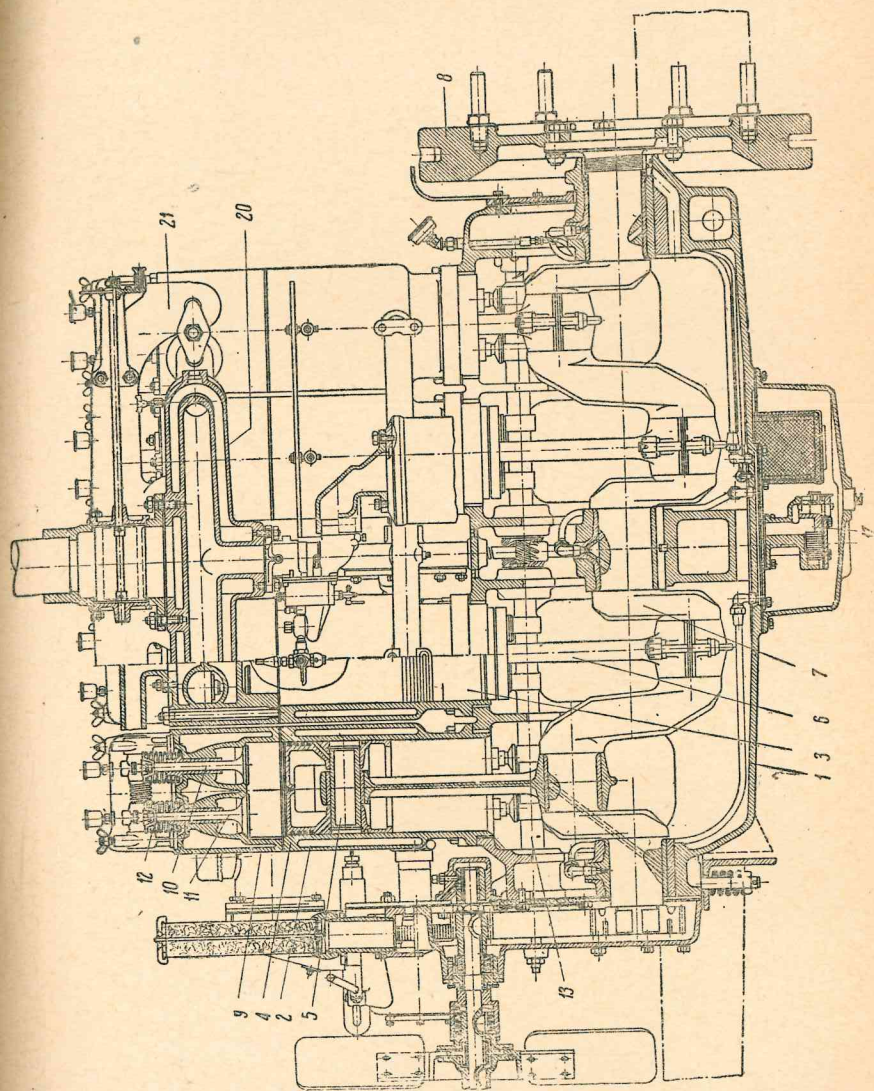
Продольный разрез двигателя «Сталинец-60» ЧТЗ
